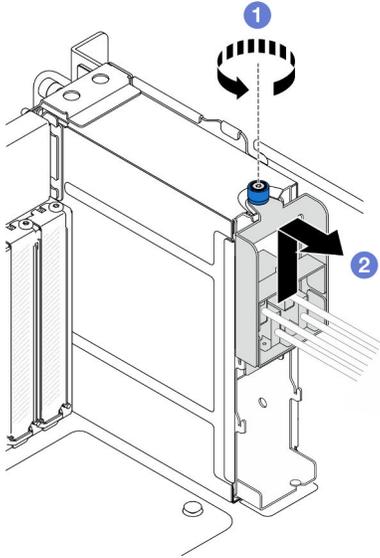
Entfernen der E3.S-Kabelbaugruppe
